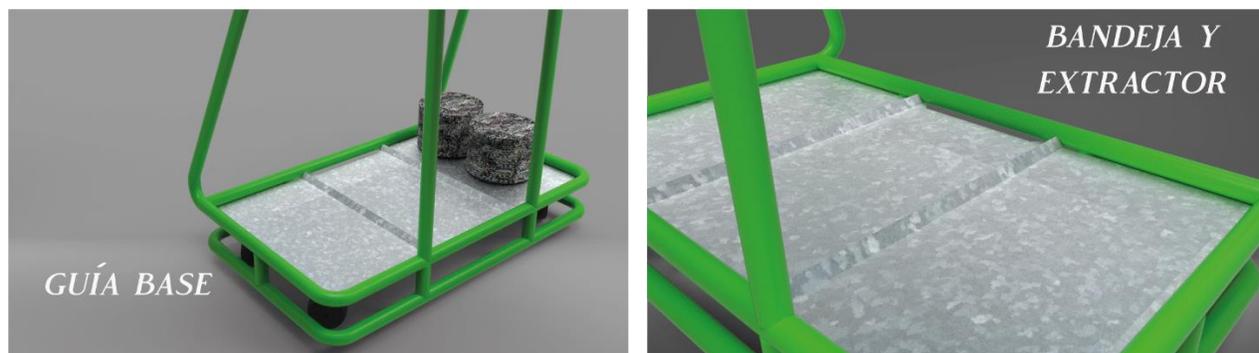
Detalles de la base – La guía para ubicación, la bandeja con las nervaduras y el extractor. Fuente. Elaboración Propia
